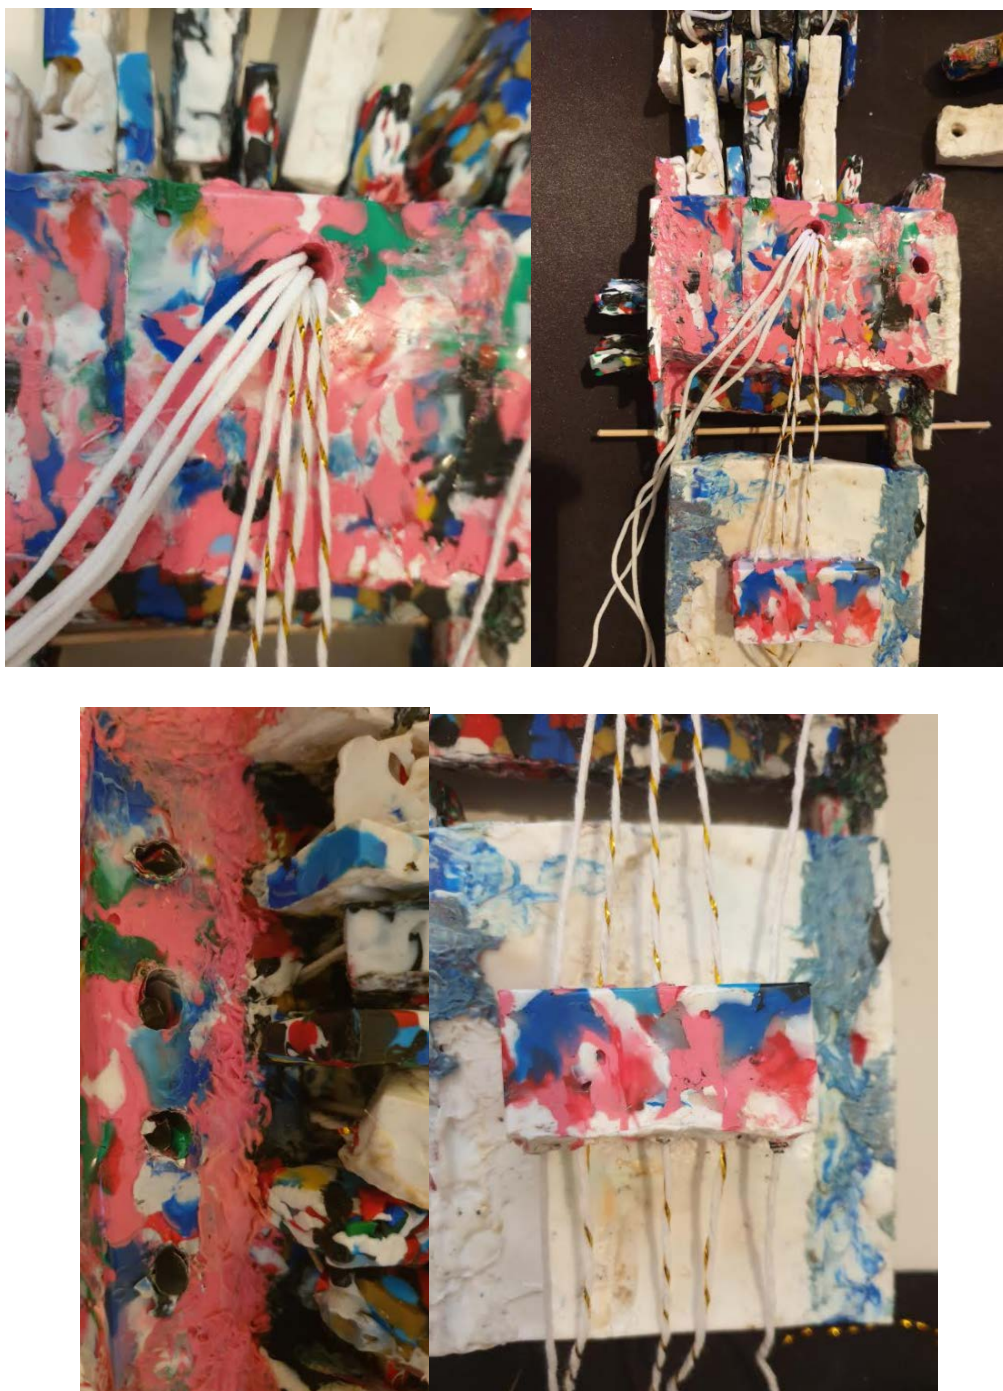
Inserción de cuerdas hasta el anclaje del brazo
